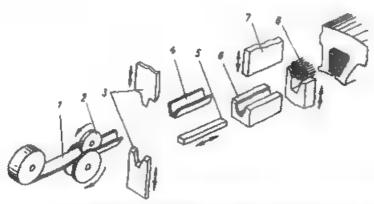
Схема работы станка для заклинивання пазов статора (назовые клиявя из узкой ленты)
